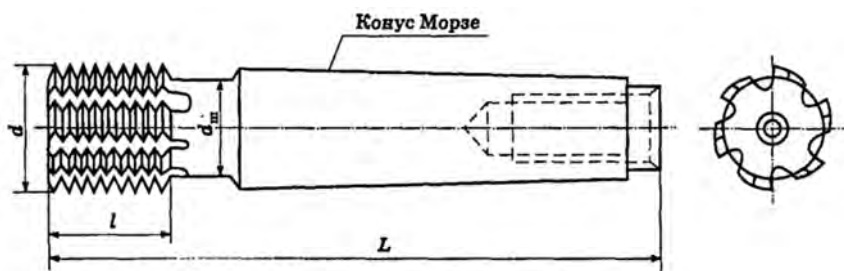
Хвостовая резьбовая гребенчатая фреза
